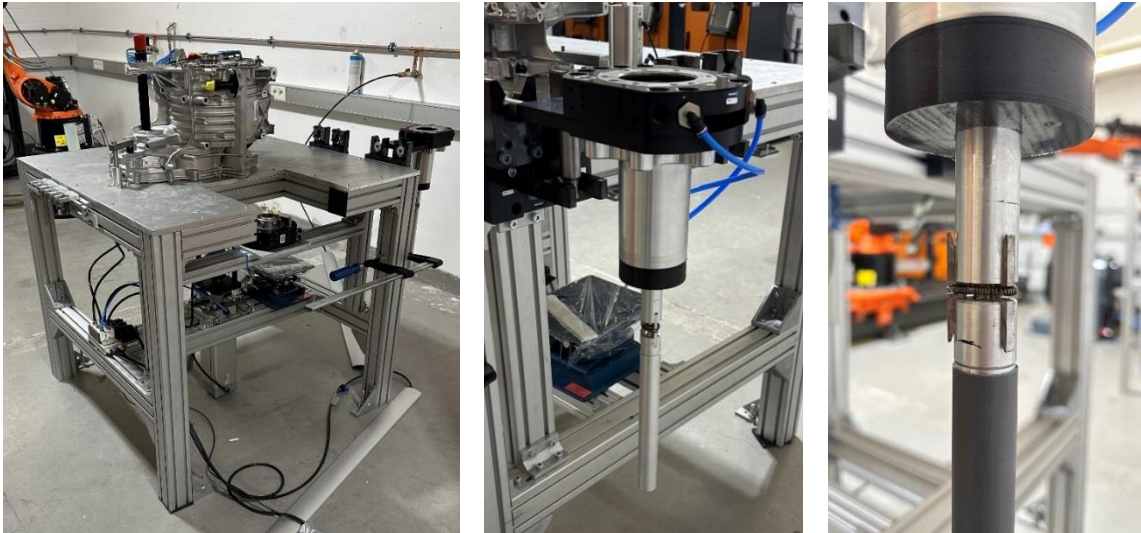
Austreibetisch für Rotor und Stator (links), Aufnahmewerkzeug für den Rotor (mitte) und Close-Up des Aufnahmewerkzeugs für den Rotor im greifenden Zustand (rechts).
